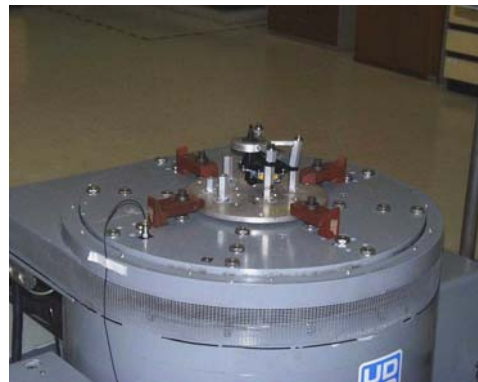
Fixação Indireta (dispositivo de fixação) – Auxílio de “unhas” laterais
